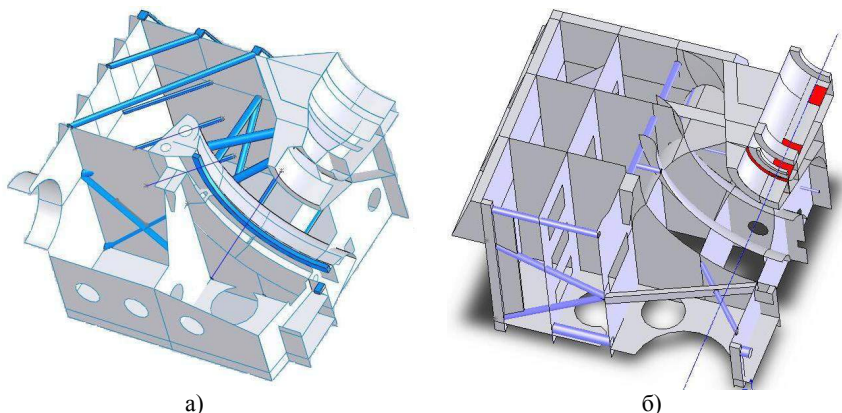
Нижняя половина наружного корпуса ЦНД: а) «сотовая» конструкция; б) стержневая
